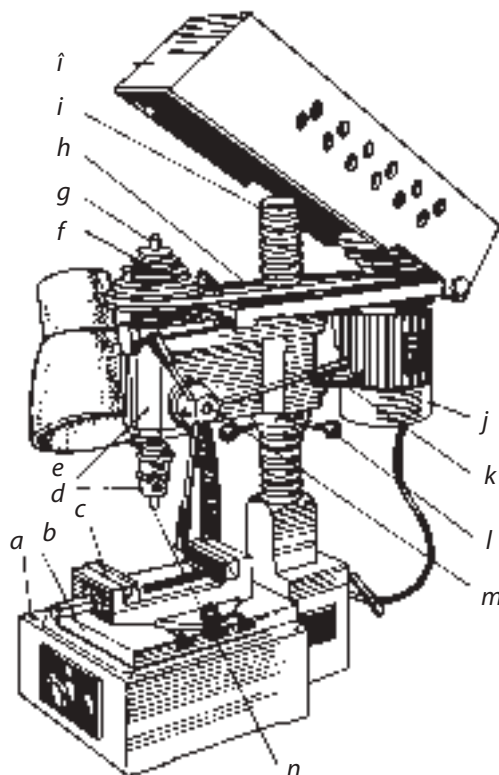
Mașină electrică de găurit: a – bază; b – masă de lucru; c – menghină; d – mandrină; e – păpușa fixă; f – roată de curea; g – arbore-portburghiu; h – curea de transmisie; i – coloană; i – manta de protecție; j – motor electric; k – mecanism de fixare a păpușii pe coloană; l – manetă de deplasare a păpușii fixe; m – roată de mână; n – burghiu.
